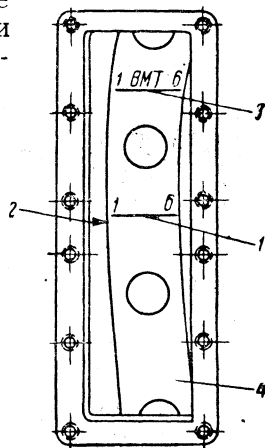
Метки на валоповоротном диске коленчатого вала:
